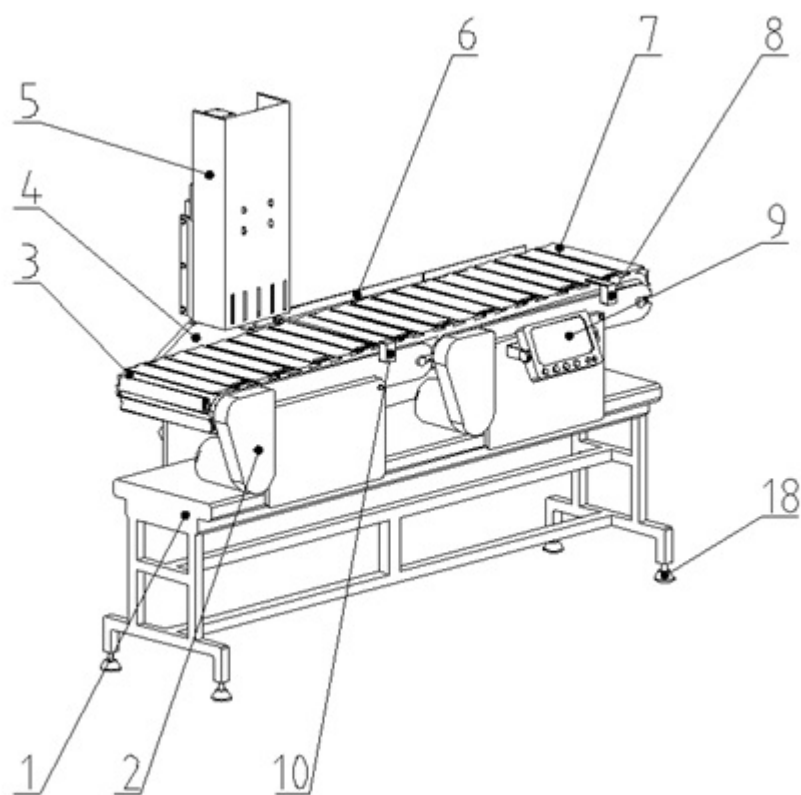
предлагаемое устройство головоотсекающей машины, вид общий
